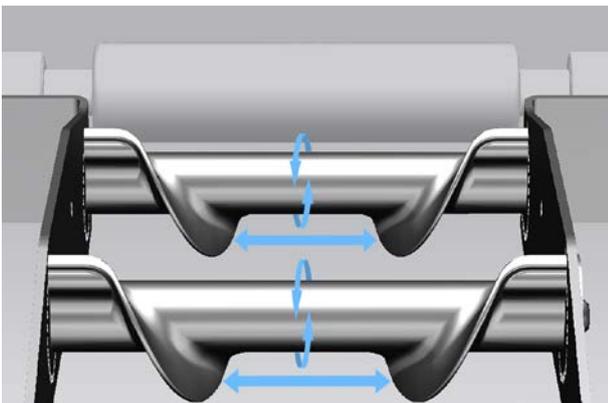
Guía de cinta patentada para obtener una calidad uniforme y reproducible
